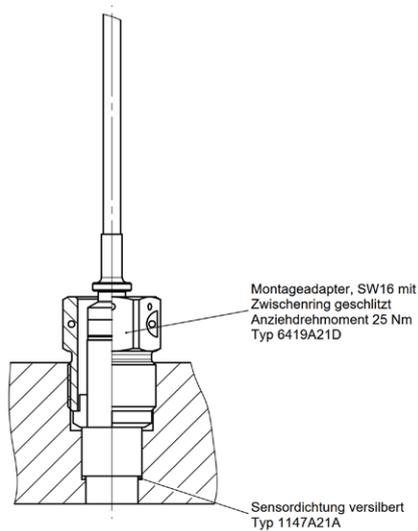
Montage mit Montageadapter Typ 6419A21D und Dichtung Typ 1147A21A
